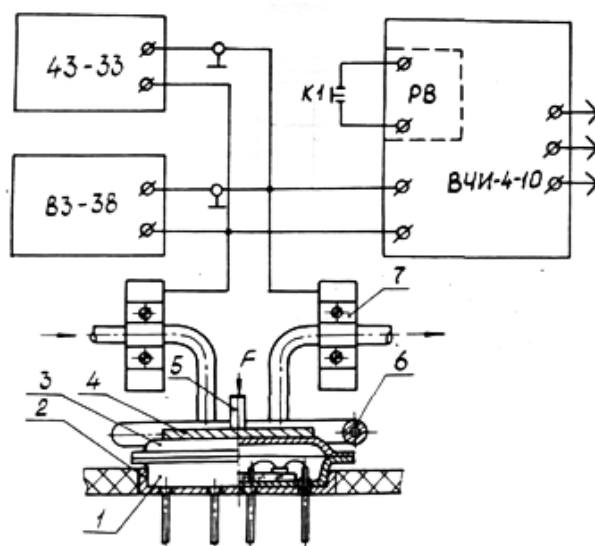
Схема устройства ВЧ-пайки корпусов БИС
